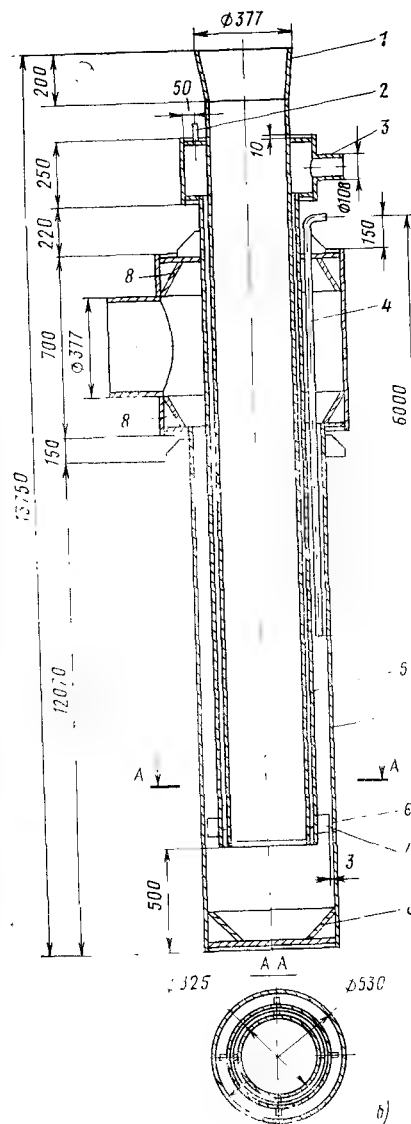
Гидрозатворы линии аварийного перелива конденсата из а) — разработка ВТИ: 1 — внутренняя труба размером 325×8; 2 — линия под розатвора; 3 — кожух; 4 — наружная труба размером 529×7; 5 — обсадная труба; 6 — устройство впуска воздуха; 7 — соединительная труба между П2 и между гидрозатвором и конденсатосборником; 8 — конденсатор; 9 — разраб 2 — воздушник; 3 — патрубок подвода конденсата для восстановления гидро пичку гидрозатвора; 5 — кожух; 6 — наружная труба; 7 — центрирующие реб
